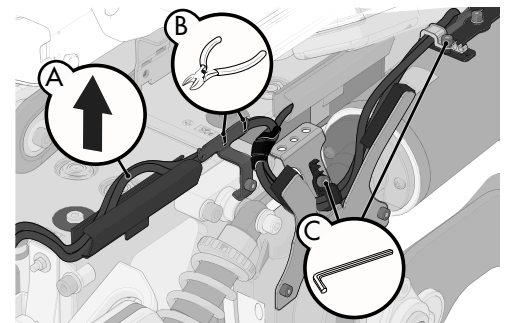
Entfernen Sie das Kabel aus seinen Befestigungen.
